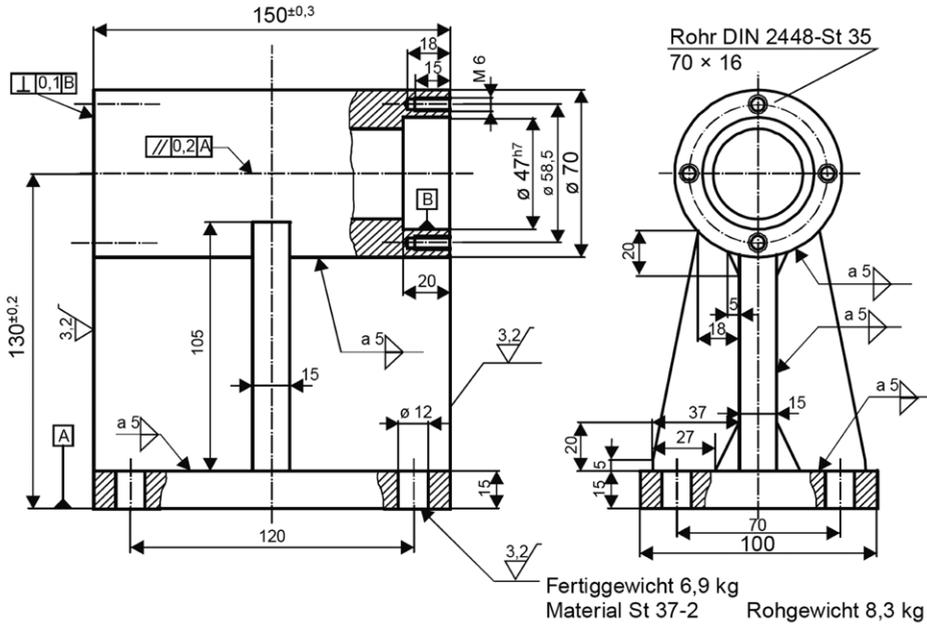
Lagerbock in Schweißausführung [15]
